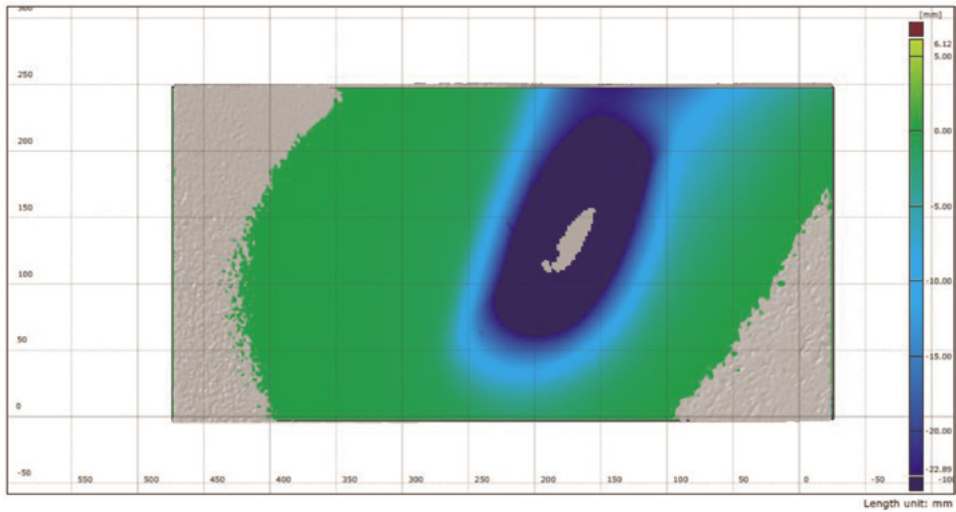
Käytöstä poistettu EN 1.4301-levy /40/
